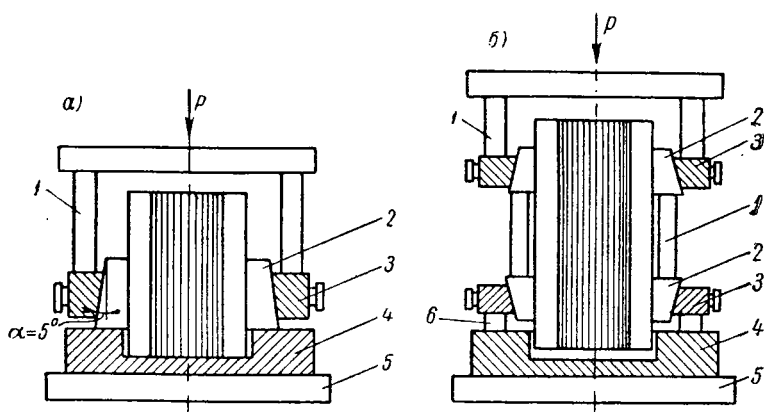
Приспособления для опрессовки цилиндра меди коллектора с двумя (а) и тремя (б) бандажными кольцами
